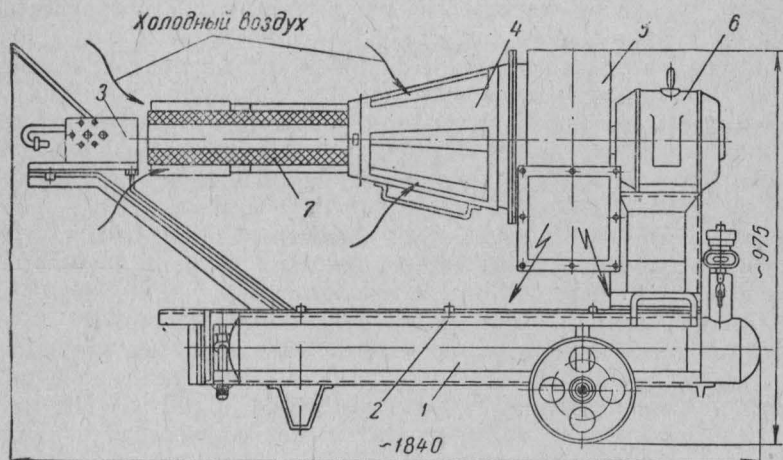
Схема воздухоподогревателя ОВЖТ-80:
